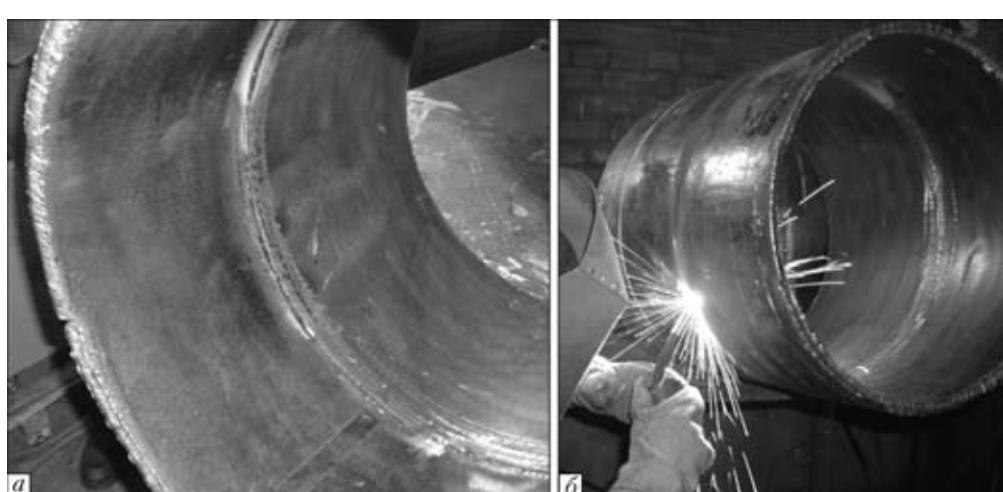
Внешний вид (а) и процесс формирования на весу обратного валика при сварке в углекислом газе на установках типа ДК (б)
